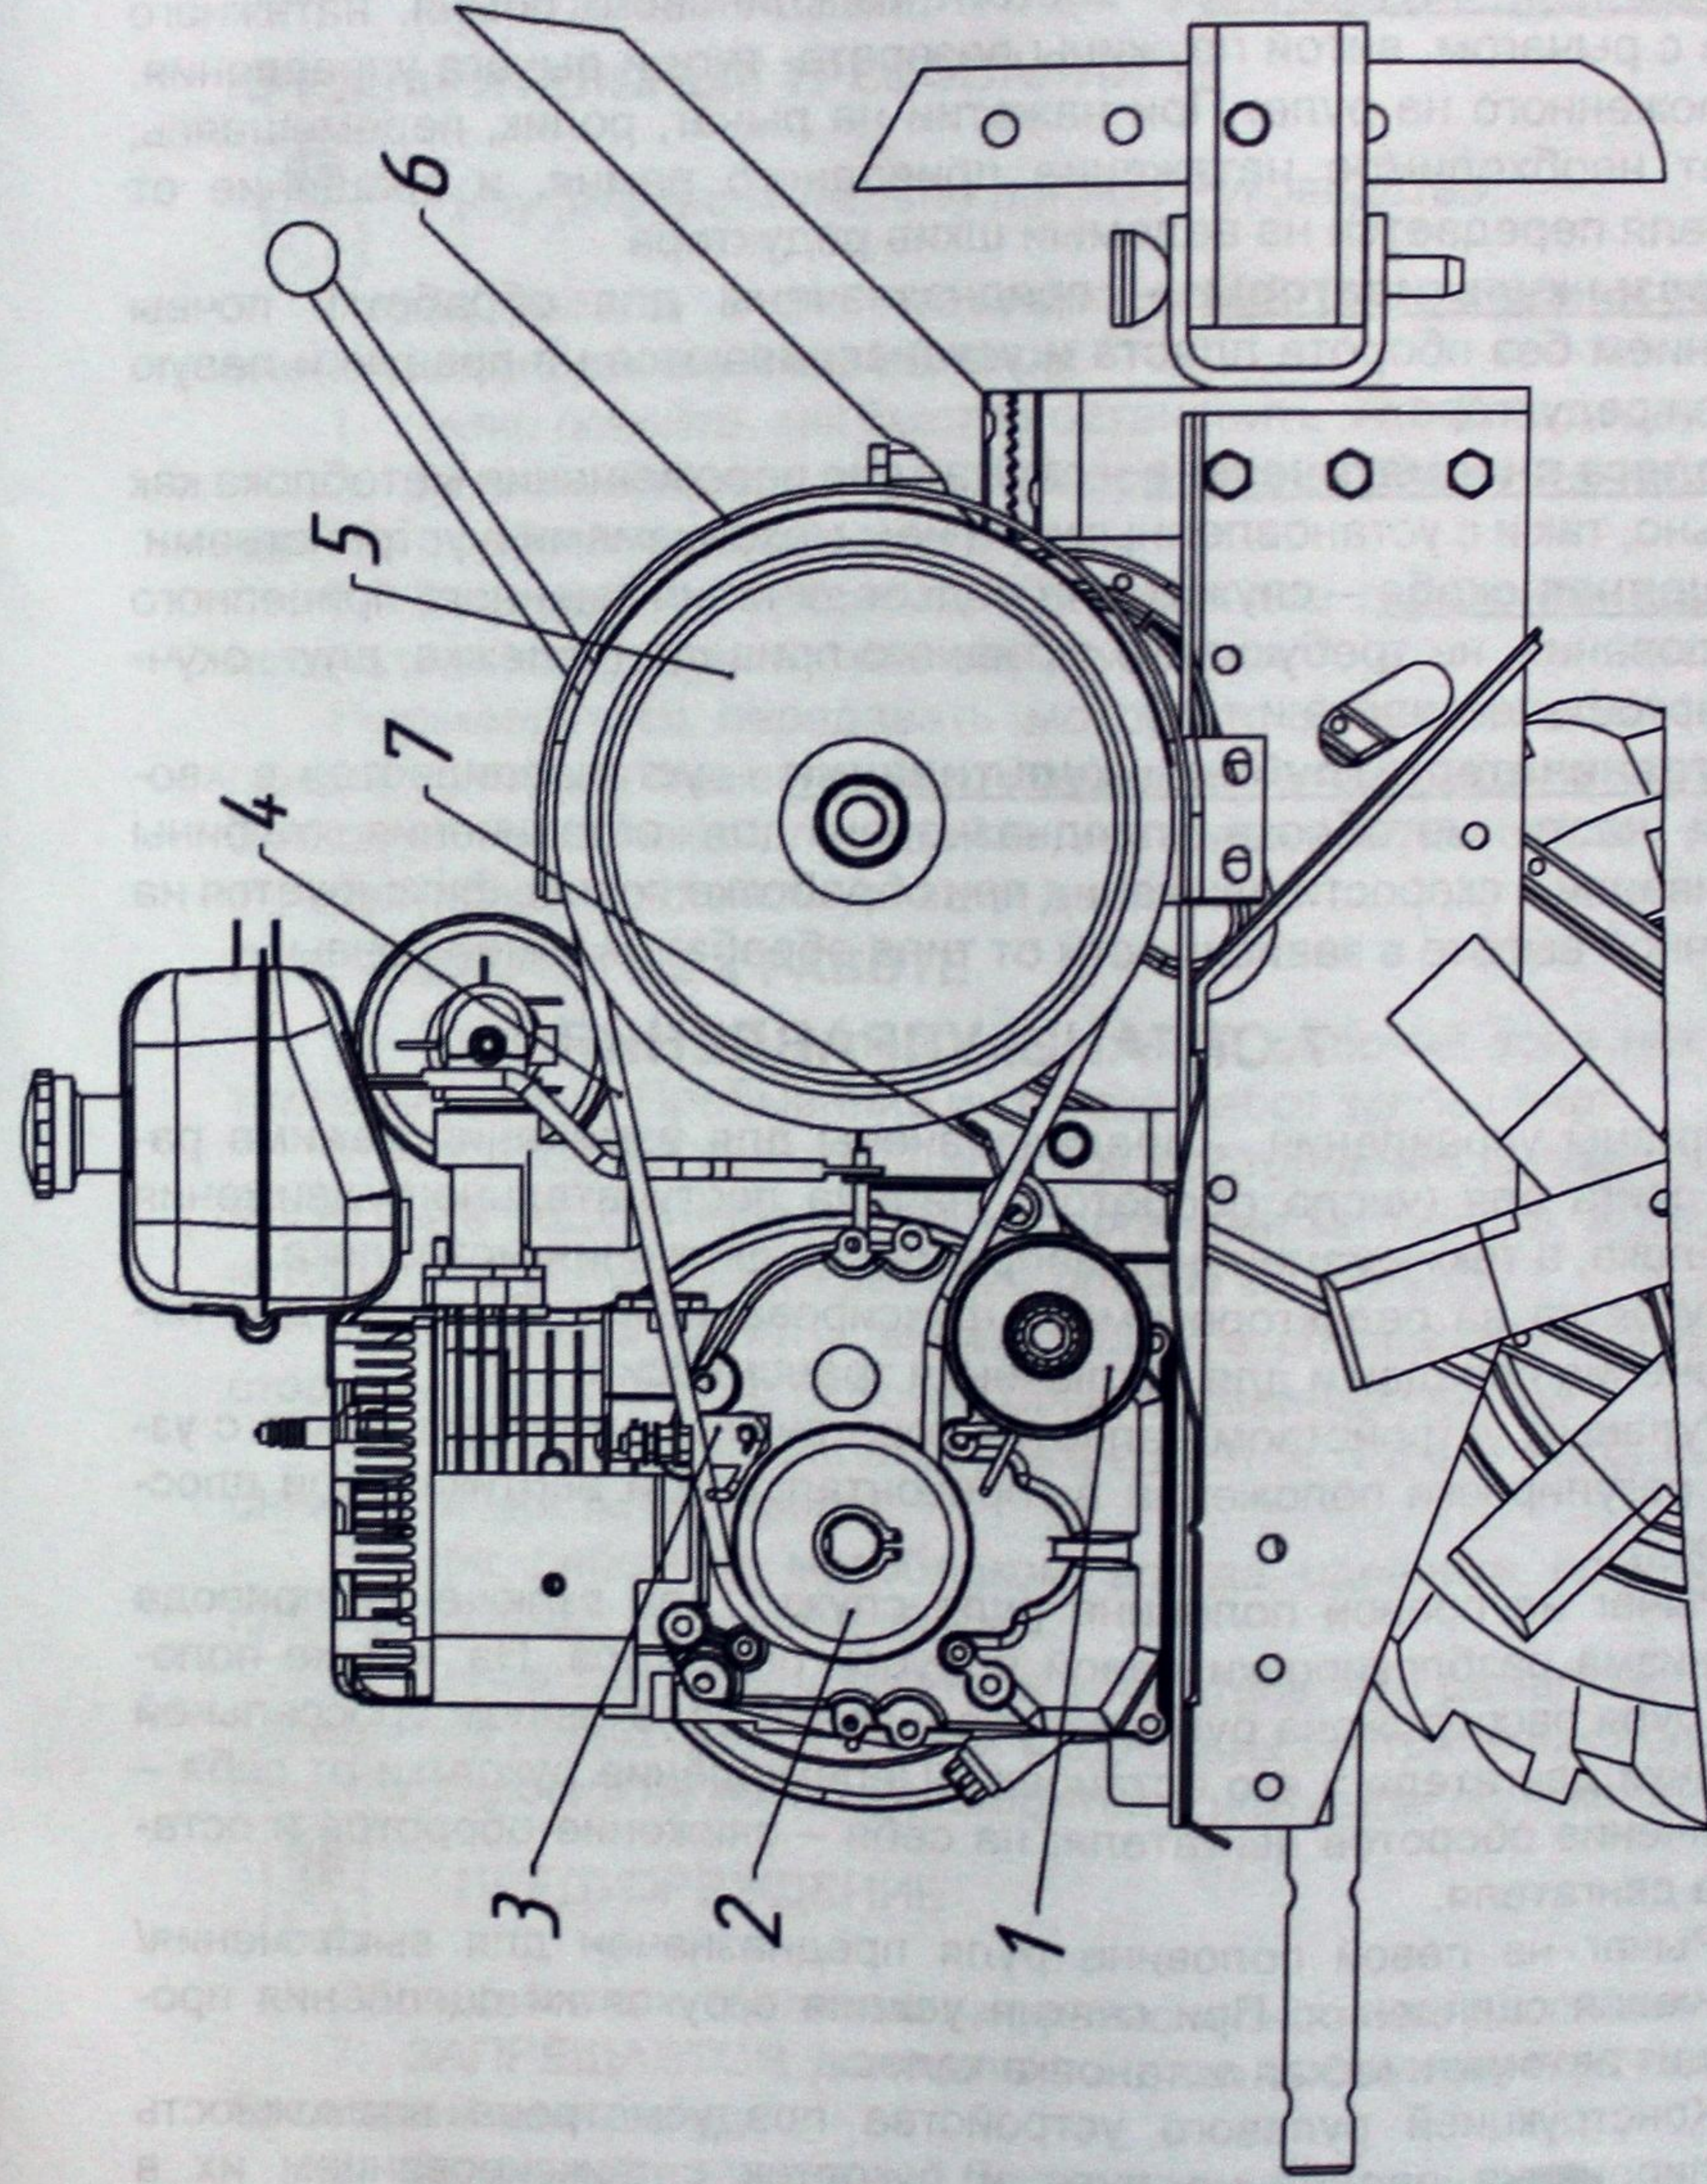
Общий вид мотоблока. Вид слева (защитный кожух снят).
